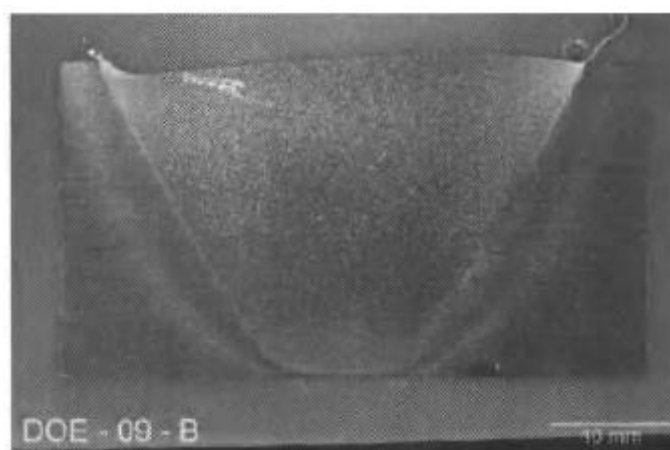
Macroestrutura de uma junta de Ti-6Al-4V com 25 mm de espessura soldada por FSW
